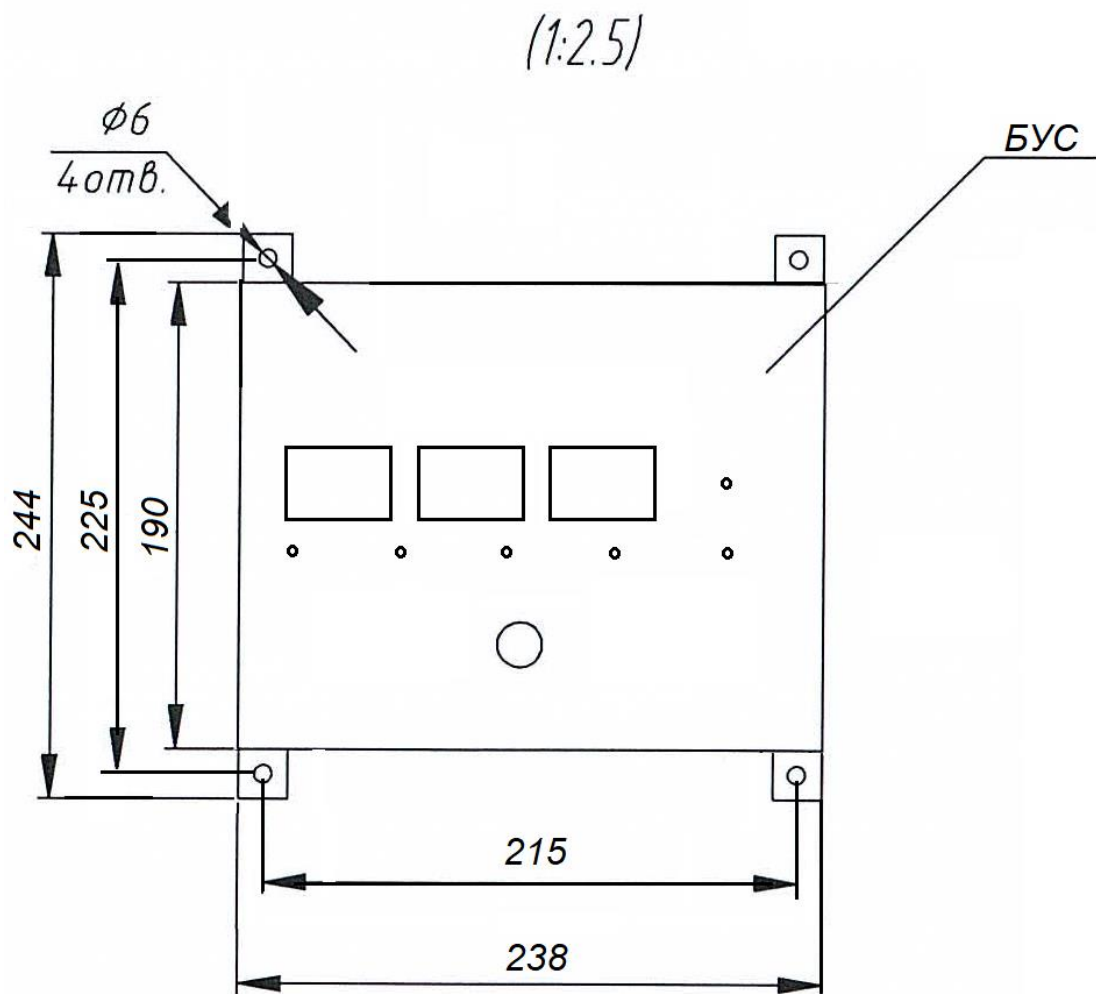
Габаритные и присоединительные размеры БУС
